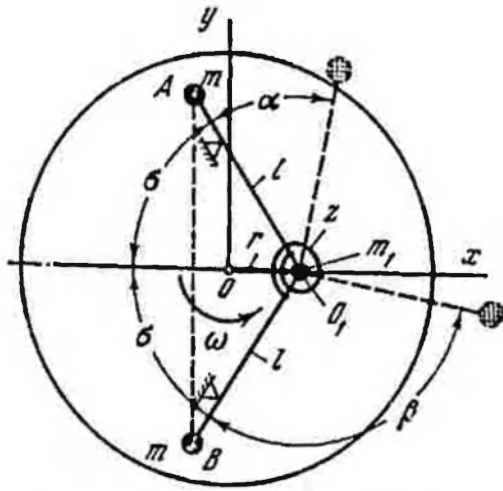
Кинематическая схема механизма вибратора с поворотными дебалансами
